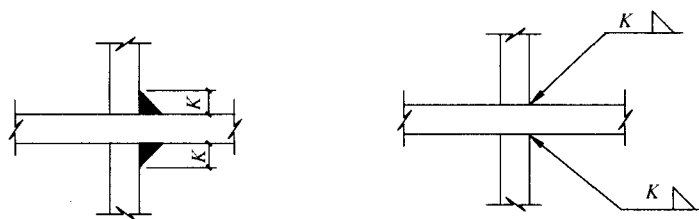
3 个及以上焊件的焊缝标注方法
